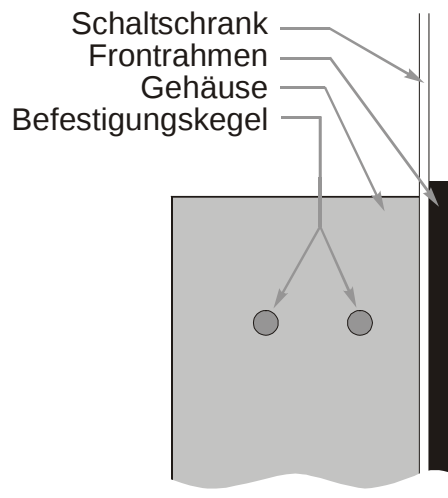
Seitenansicht - ohne Befestigungsklammer
